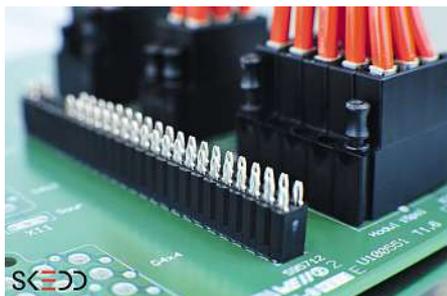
Board-to-board-Steckverbinder in SKEDD-Technologie
